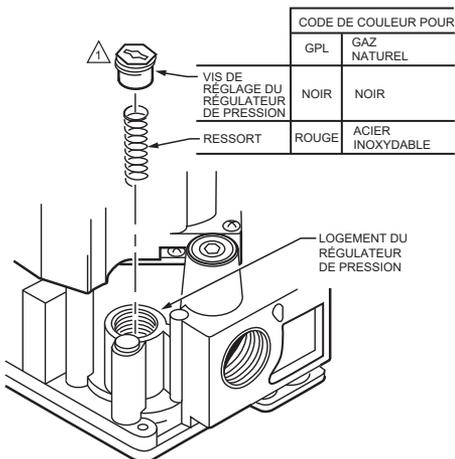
Vue de haut des régulateurs à gaz combinés VR8215S, T.
